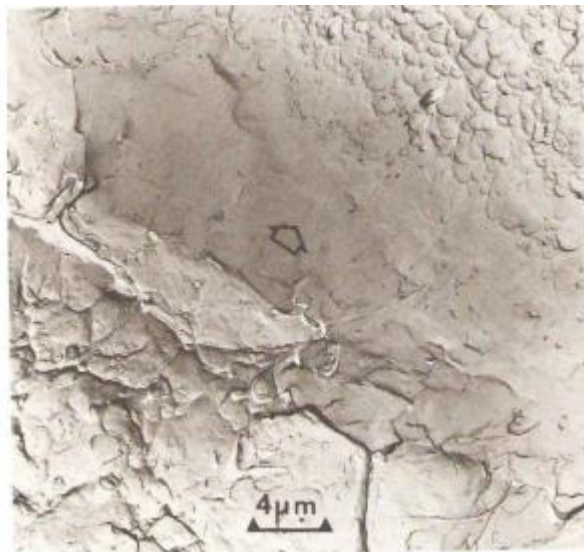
Zona extendida justo antes de la fractura final en acero de alta resistencia fatigado. Fuente: [3]
